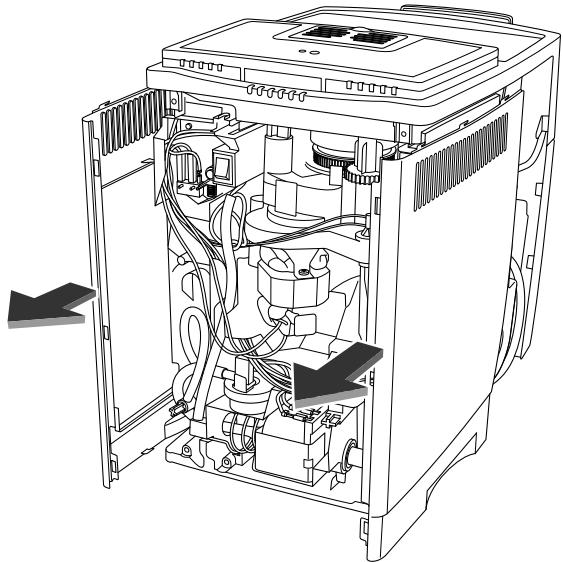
SMONTAGGIO CRUSCOTTO
